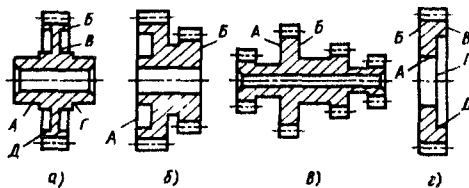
Базовые поверхности цилиндрических зубчатых колес:
